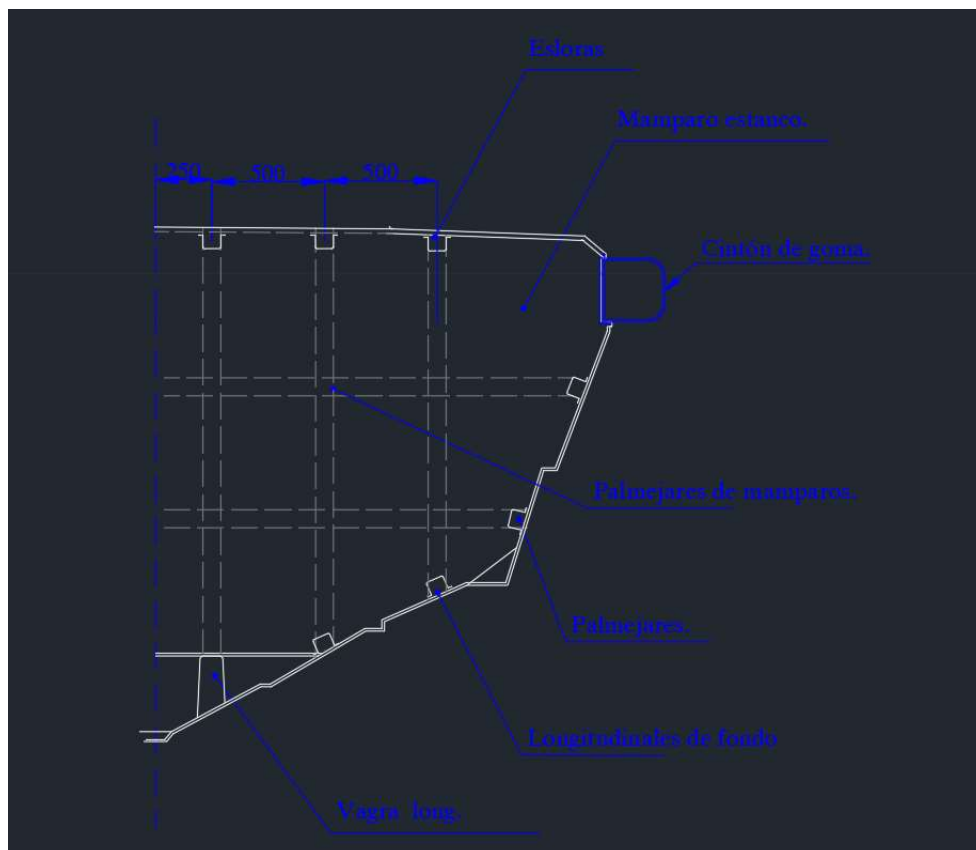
Mamparo y refuerzos de la P12 NASAI IPS. Fuente propia
